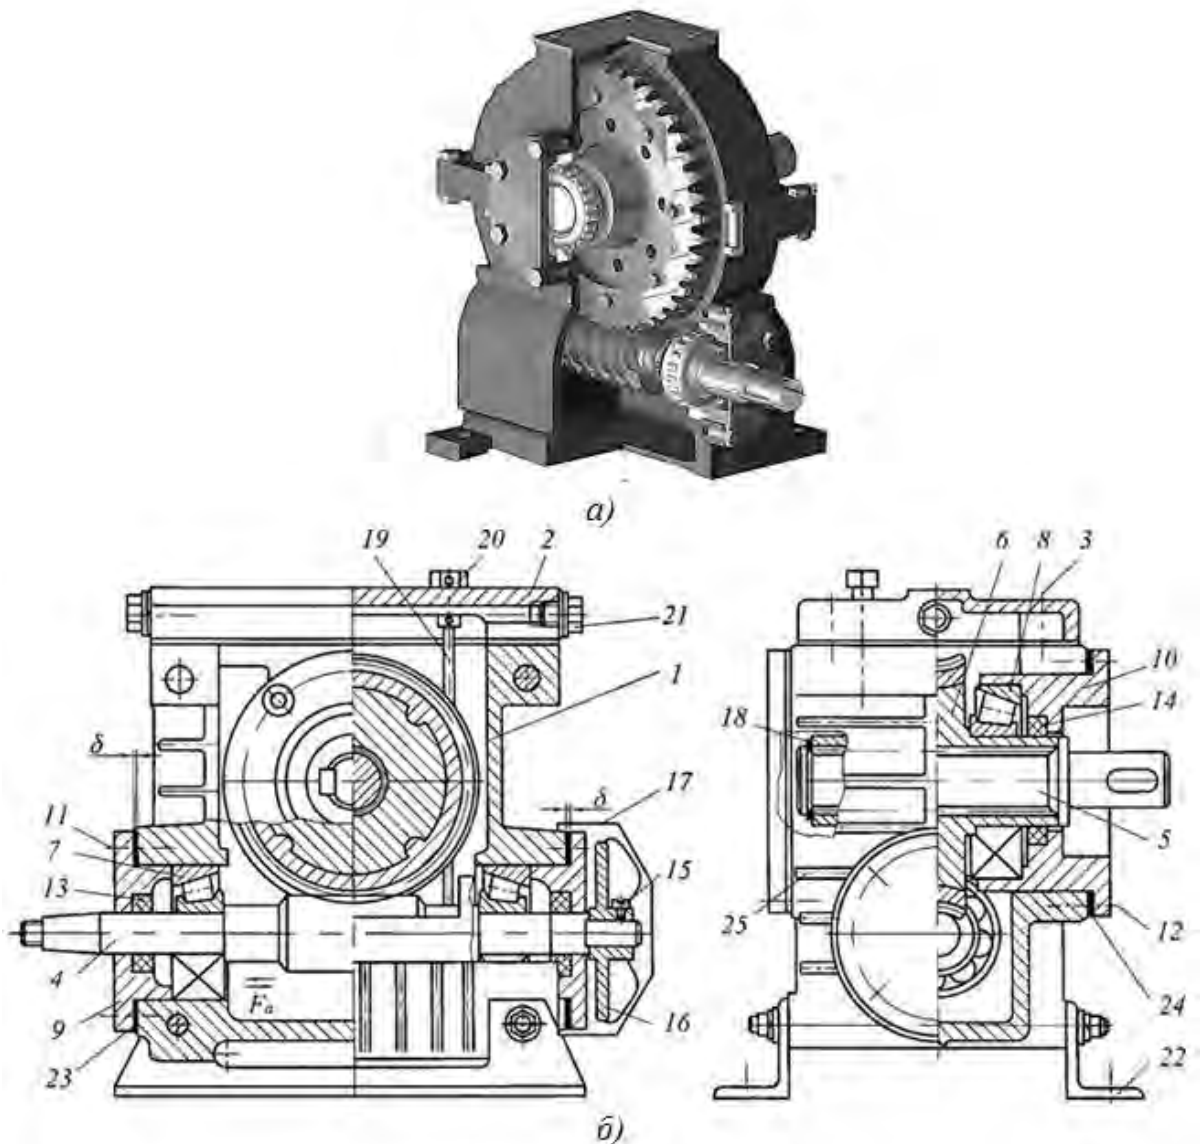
Черв'ячний редуктор: загальний вигляд (а) та креслення (б)
